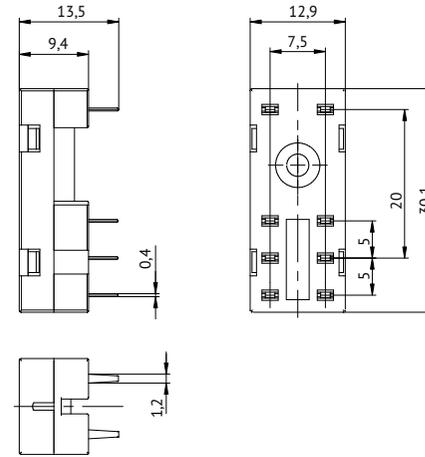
Габаритные, установочные и присоединительные размеры розеток OptiRel G RR95-12
